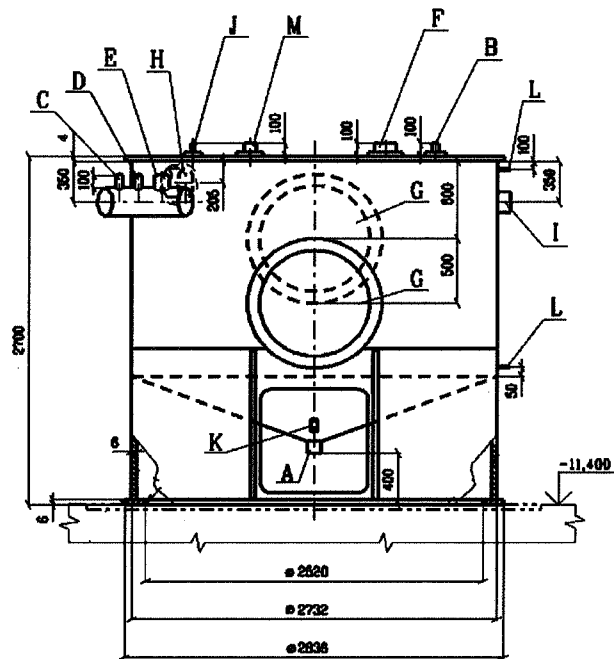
Габаритный чертеж бака-приямка трапных вод с гидрозатвором с
